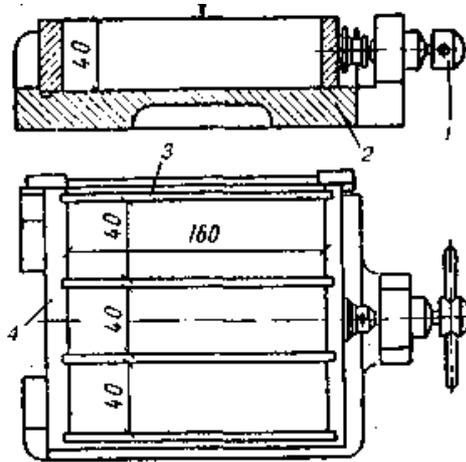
Форма для виготовлення зразків-балочок
